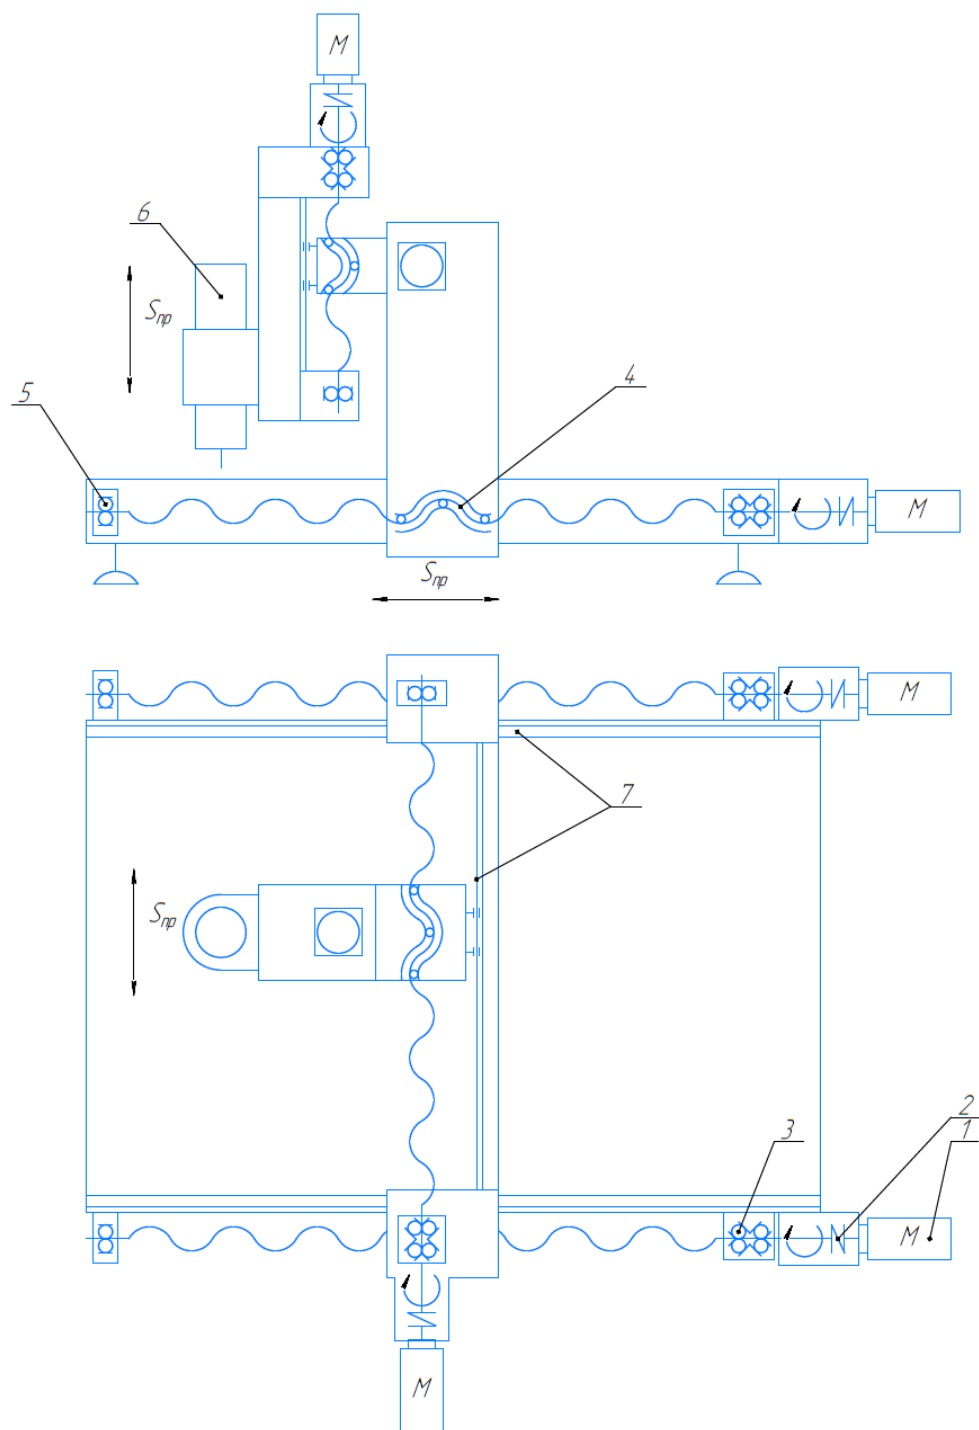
Кинематическая схема фрезерно-гравировального станка с ЧПУ
